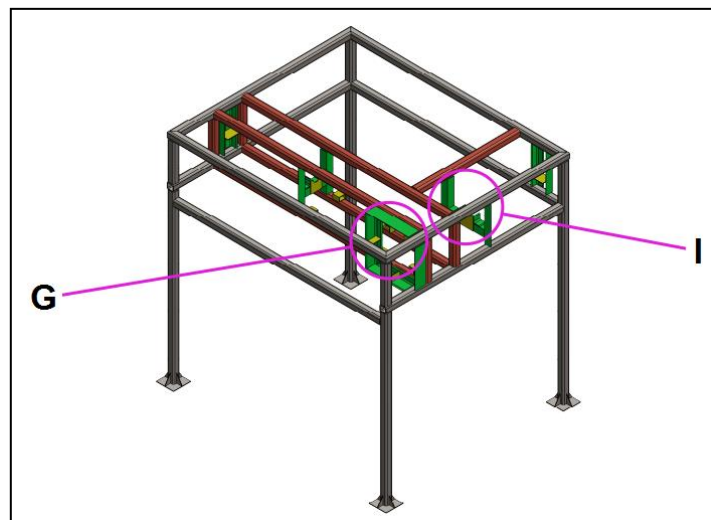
Vista de las secciones G e I de la estructura de la peladora y picadora de piñas
